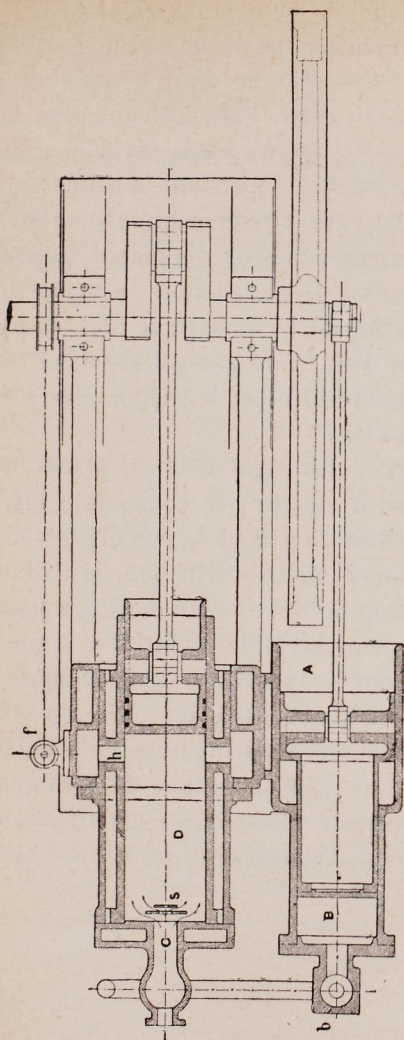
Moteur Béniér : plan-coupe horizontale.
